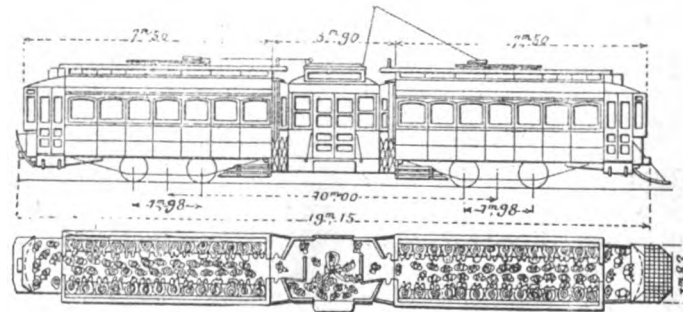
Vista e pianta di una carrozza doppia delle tramvie di Boston.
